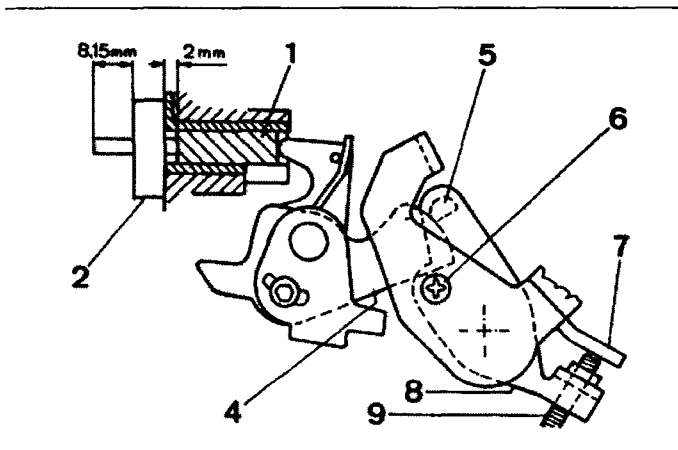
Установка пусковых оборотов - "прогрев"
